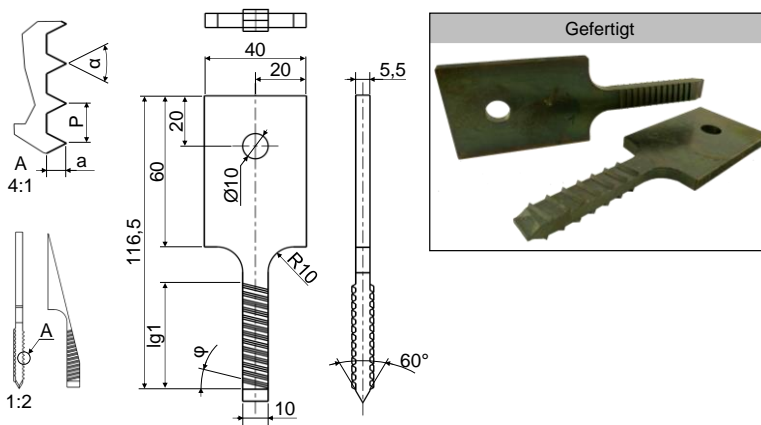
Gewinde-Testobjekte des Experimentalaufbaus zum Schrauben-Testing zur Untersuchung der Gewindeparameter: Flankenabstand P , Profilhöhe a , Flankenwinkel α und Steigungswinkel φ . Abhängig von diesen Parametern ist die Gewindelänge $lg1$. Darstellung auf Grundlage von (Hölz, Dörner, Hohlweg & Matthiesen, 2022)
